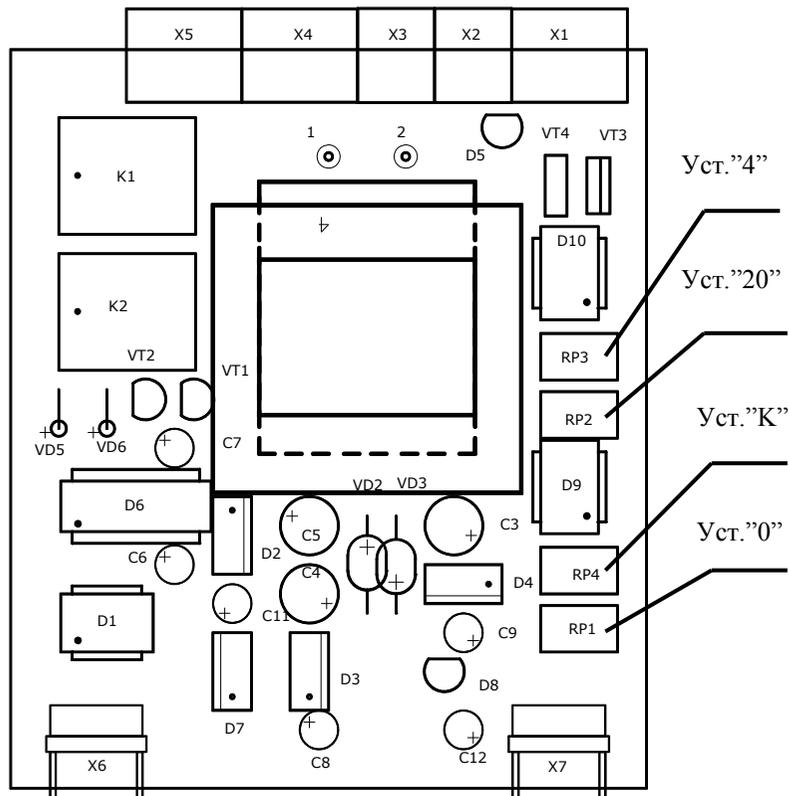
Элементы регулировки прибора ПКЦ-1Д
